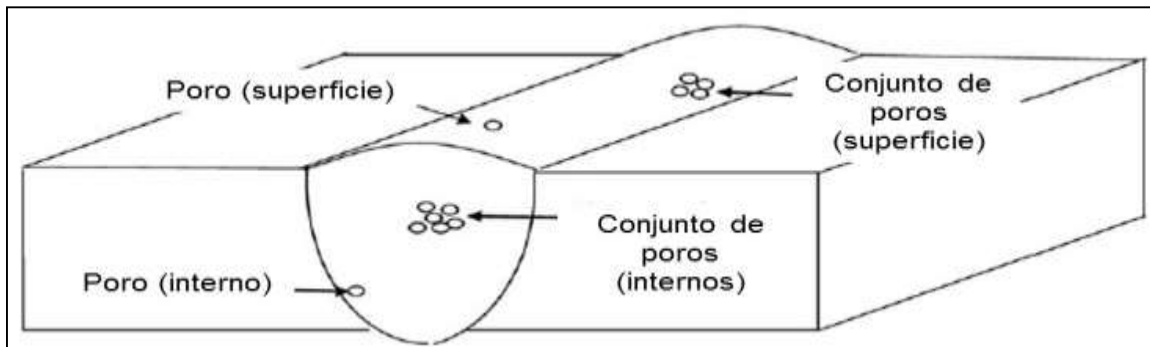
13. Porosidad en pieza soldada (20)
